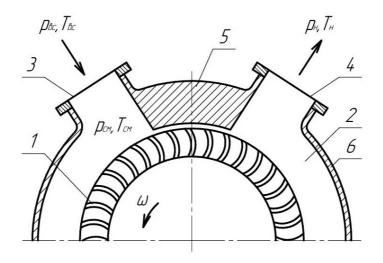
Схема вихревой ступени с двусторонним периферийно-боковым каналом, боковыми серповидными лопатками с покрывным диском:
